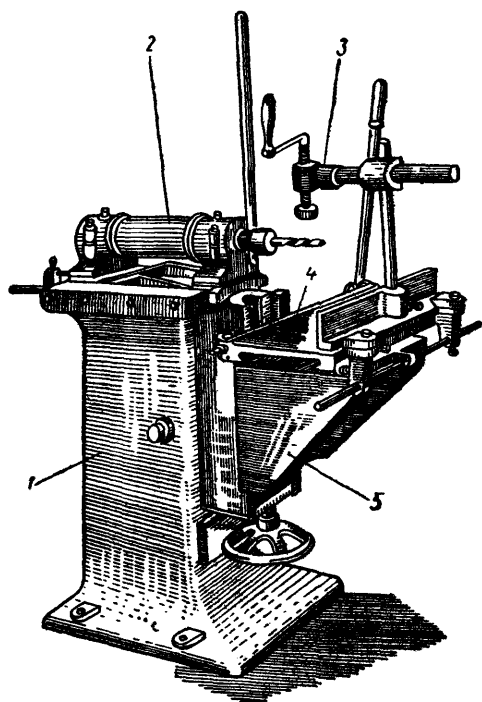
Горизонтальный сверлильно - пазовальный станок Св ГД-3
